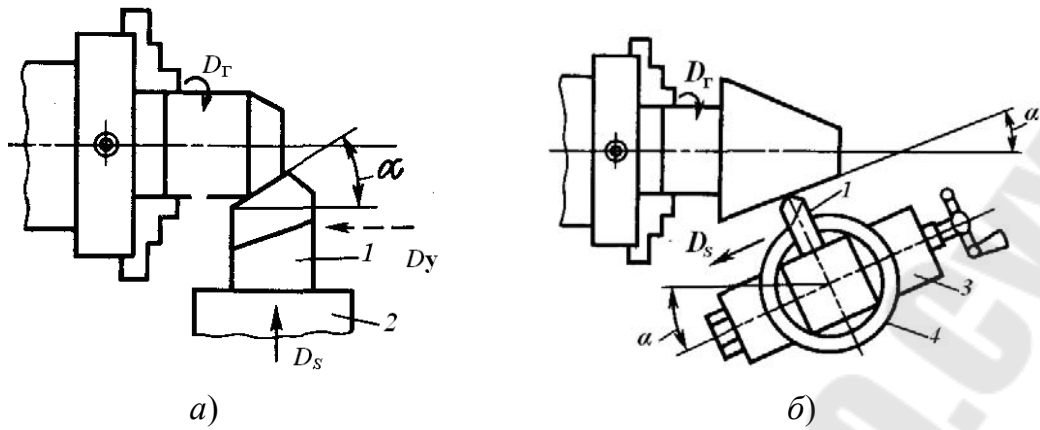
Схемы обработки конических поверхностей на токарно-винторезном станке:
